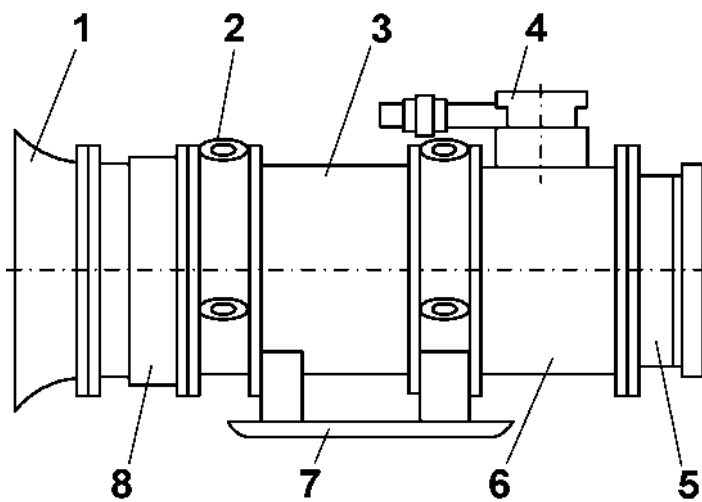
Общий вид вентилятора ВМ-6 (ВМ-6/1): 1 - подвод с решеткой; 2 - рым (проушина); 3 - корпус; 4 и 6 - ввод силового кабеля и электродвигатель РВ; 5 - выходной патрубок; 7 - салазки; 8 - противосрывное устройство
